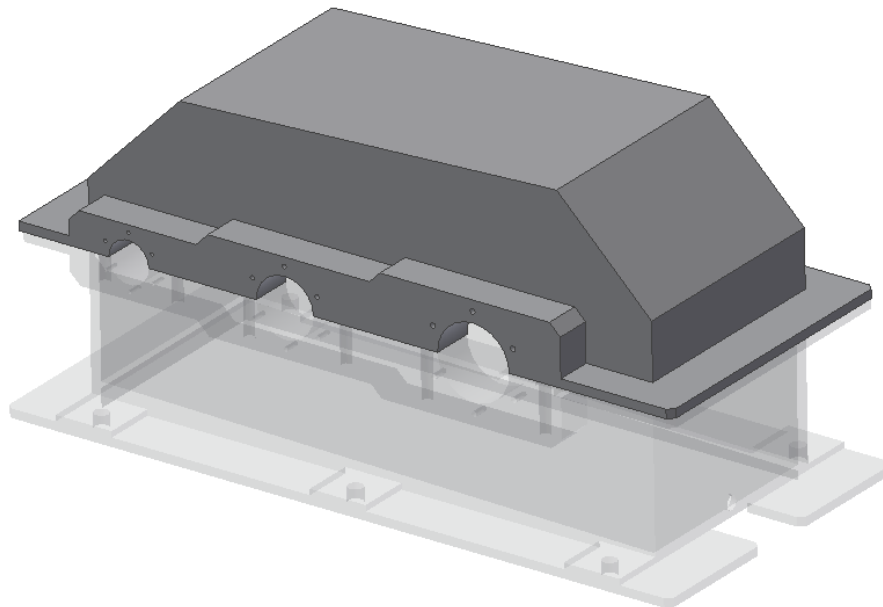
Presentación de las planchas soldadas de la tapa de la carcasa.
